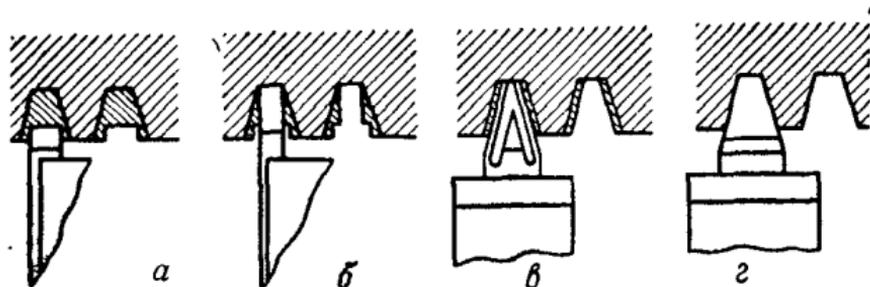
Схема нарезания трапециoidalной резьбы быстрорежущими резцами:
